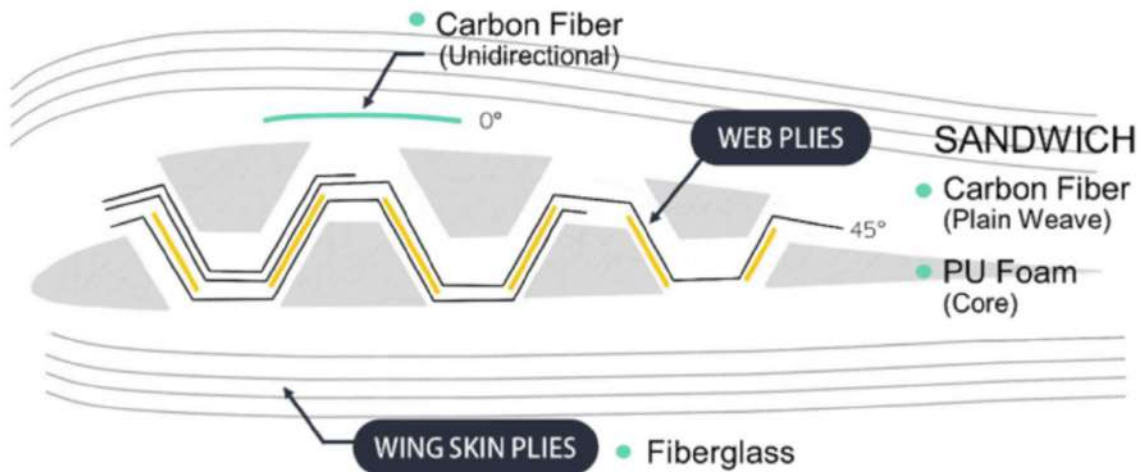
Posible concepto para perfil semihueco con estructura trapezoidal y cores de espuma
